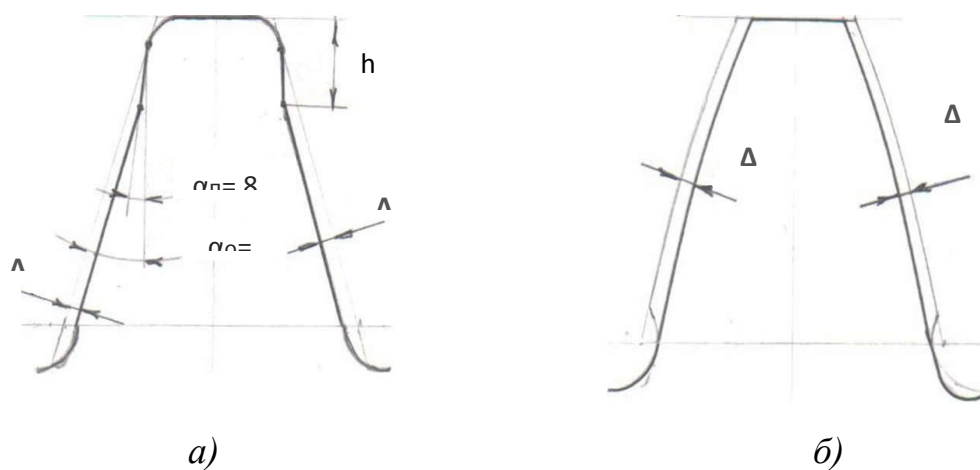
Попереднє нарізування зубів колеса: а - зуб черв'ячної фрези з «протуберанцем»; б - зуб колеса оброблений з припуском - Δ : h - висота «протуберанця», α_0 - кут вихідного профілю, α_p - кут профілю «протуберанця»
